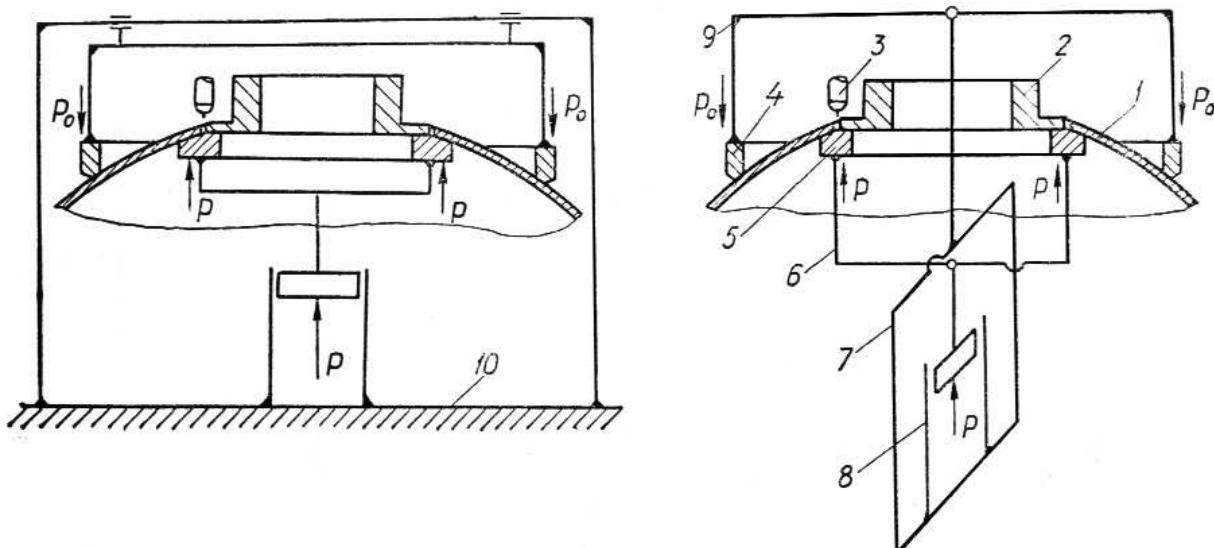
Принципові схеми пристрій для вварювання фланців у сферичні оболонки
